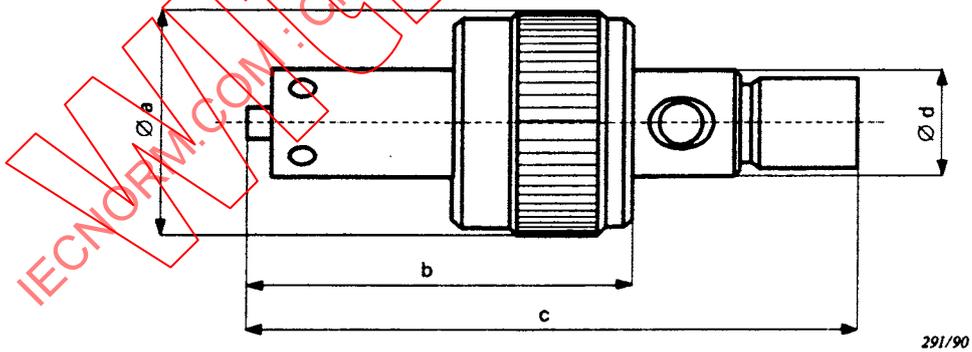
Dessin d'encombrement (pour les dimensions, voir tableau A2)
